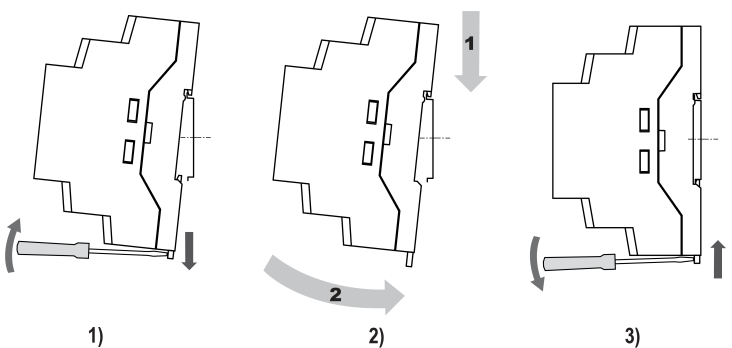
Монтаж прибора с креплением на DIN-рейку
